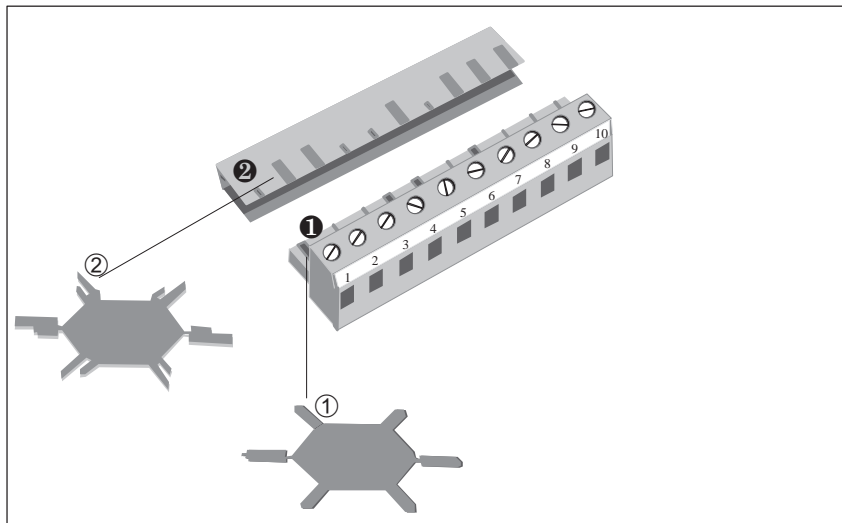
So wird verhindert, daß Stecker vertauscht werden
